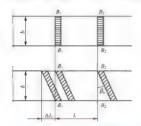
直齿轮和斜齿轮的基圆杆面展开图
